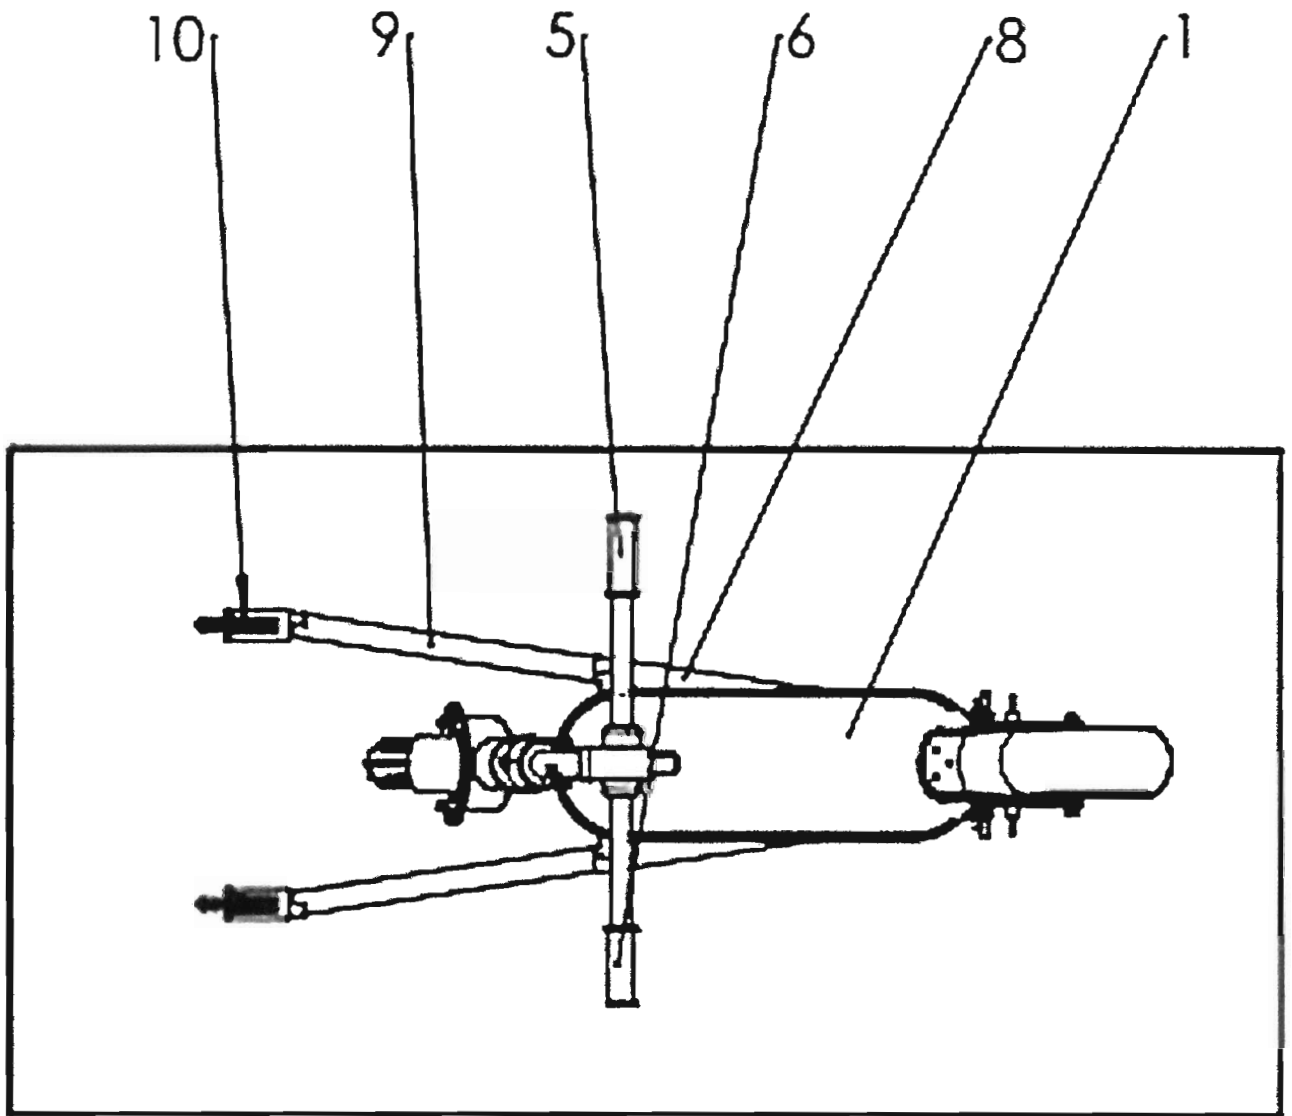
Trotineta electrică cu sistem antirăsturnare – varianta constructivă 1
